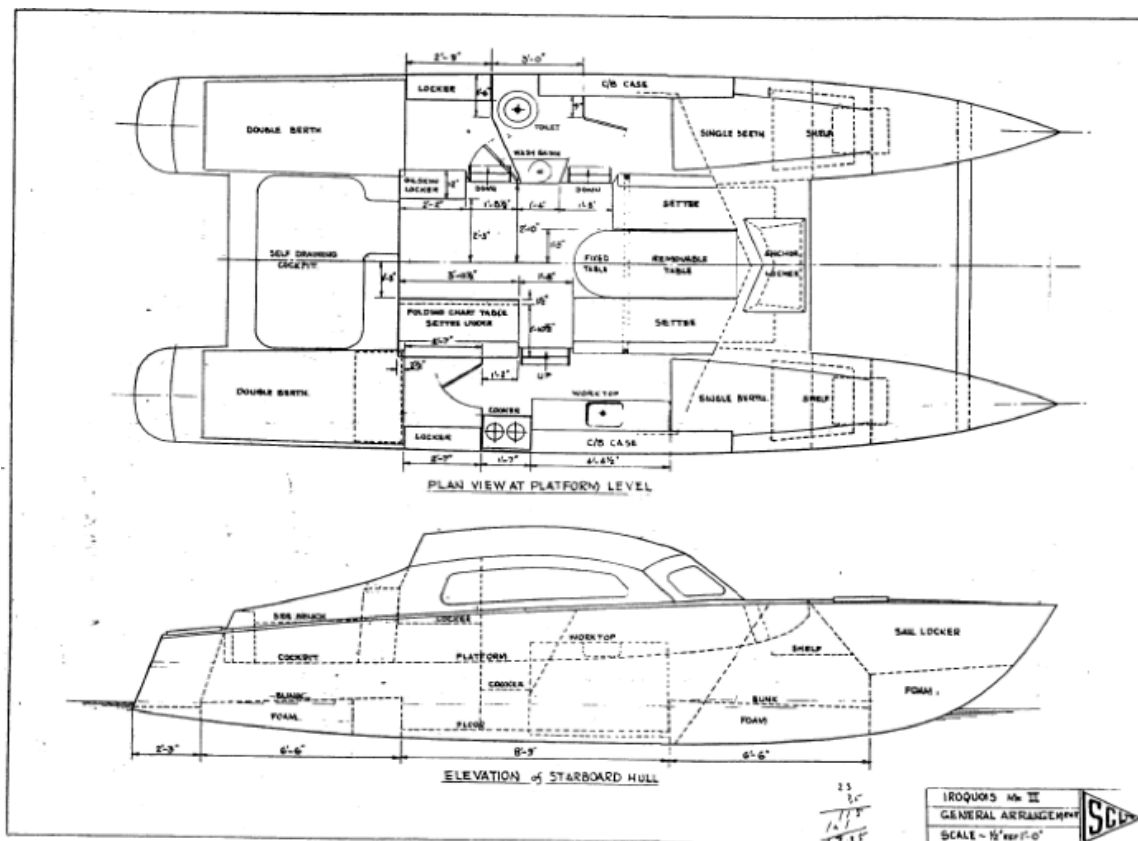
Planos en perfil y planta del Iroquois 30. Fuente: desconocida
